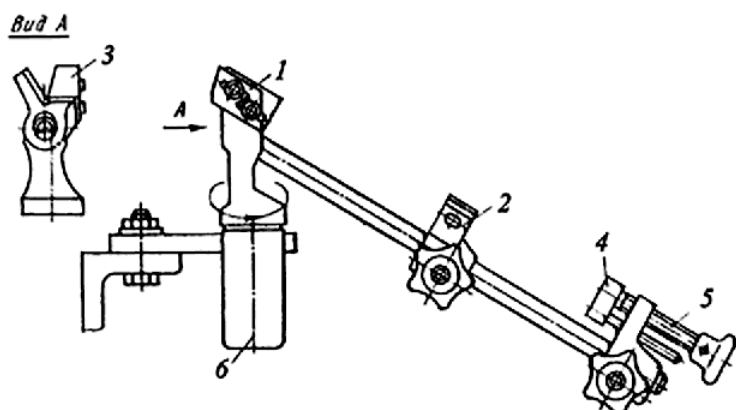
Приспособление для заточки сверла с цилиндрической задней поверхностью
